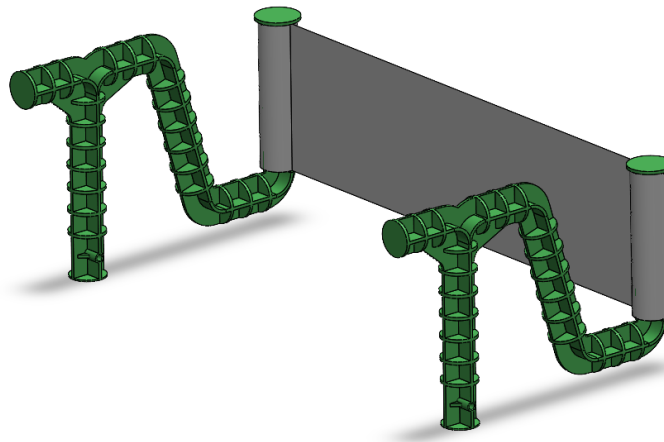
| Ensamblaje de respaldo planteado
